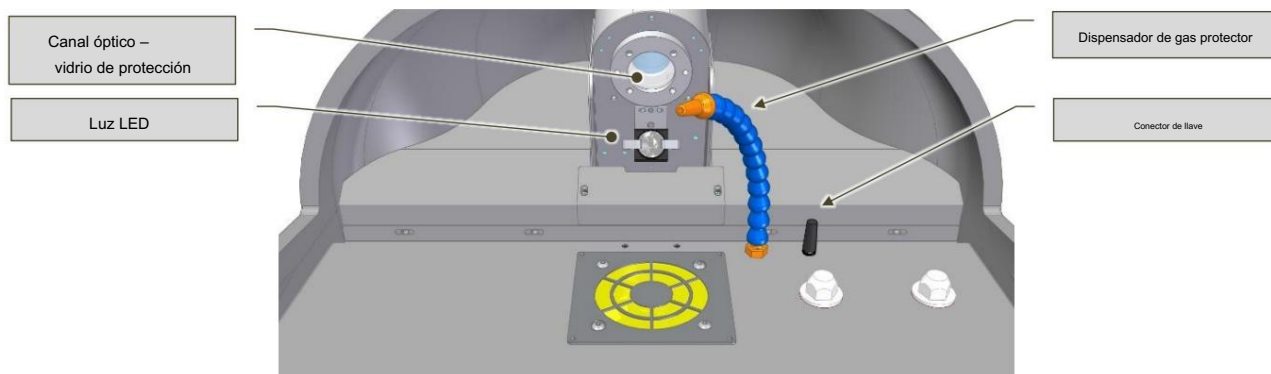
Canal óptico – vista desde la cámara de soldadura
